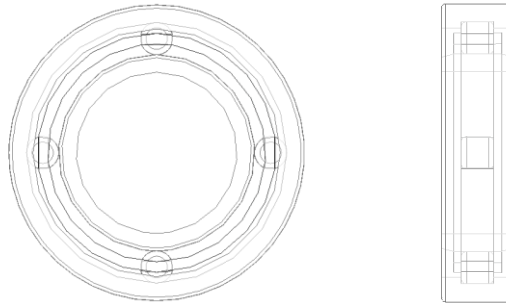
Vista lateral y frontal de Rodamiento del eje C.
